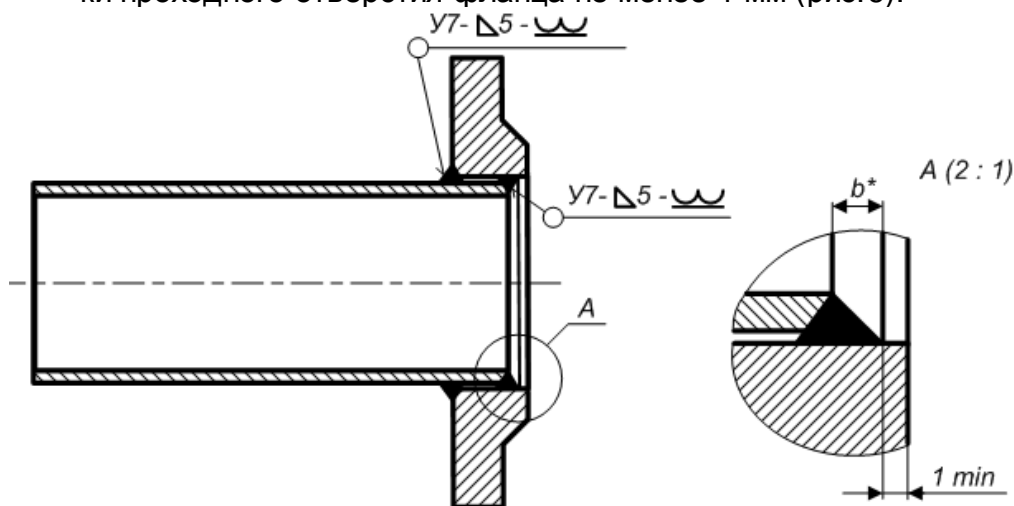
Приварка фланца к прямолинейному отрезку трубы.
